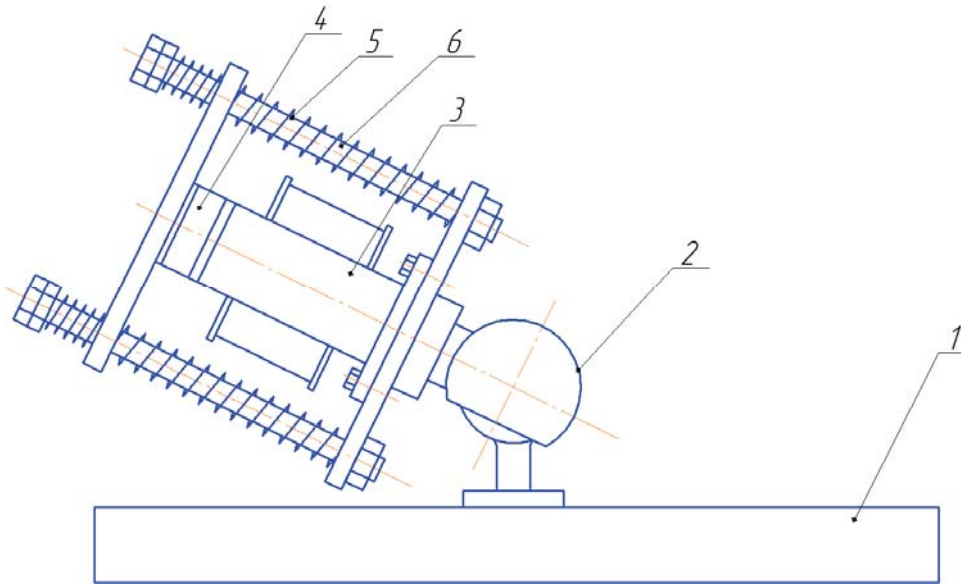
Конструктивна схема нового вібраційного пересувного пристрою з внутрішнім ступенем вільності: 1 – платформа; 2 - просторовий шарнір; 3, 4 – статор і якорь електромагнітного віброприводу, 5 - циліндричні пружини; 6 – направляючі пружин
